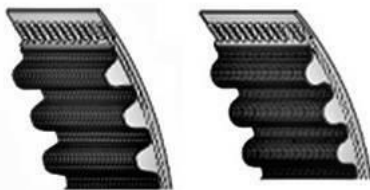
Зубчатый ремень типа ПУ-100 RPP8
